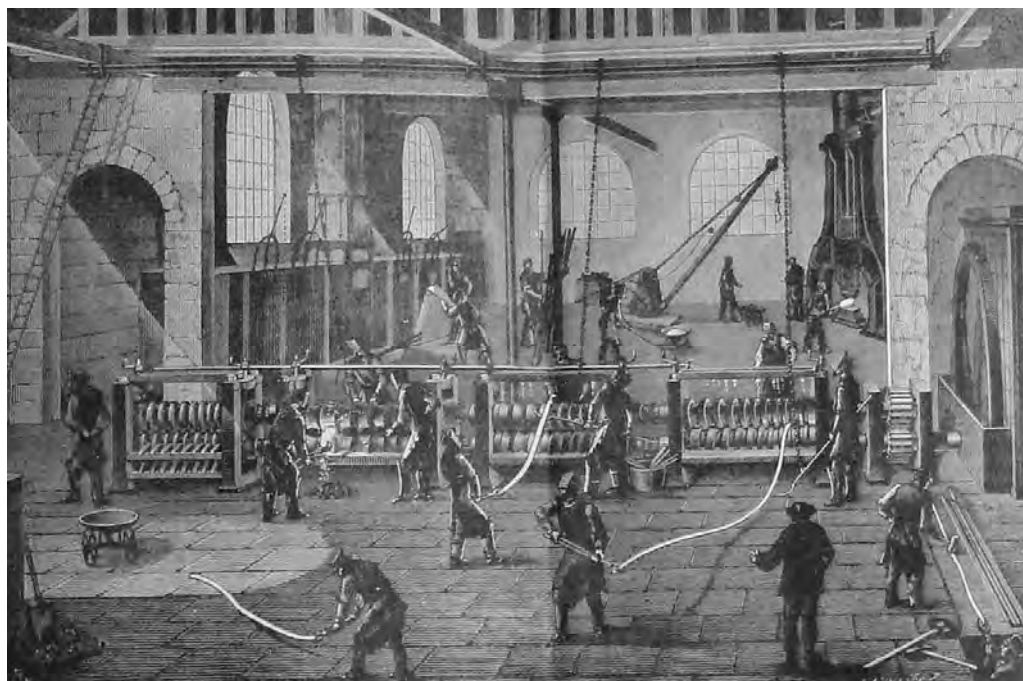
Walce zaprojektowane przez Johna Payne do produkcji prętów okrągłych, 1728 r.
